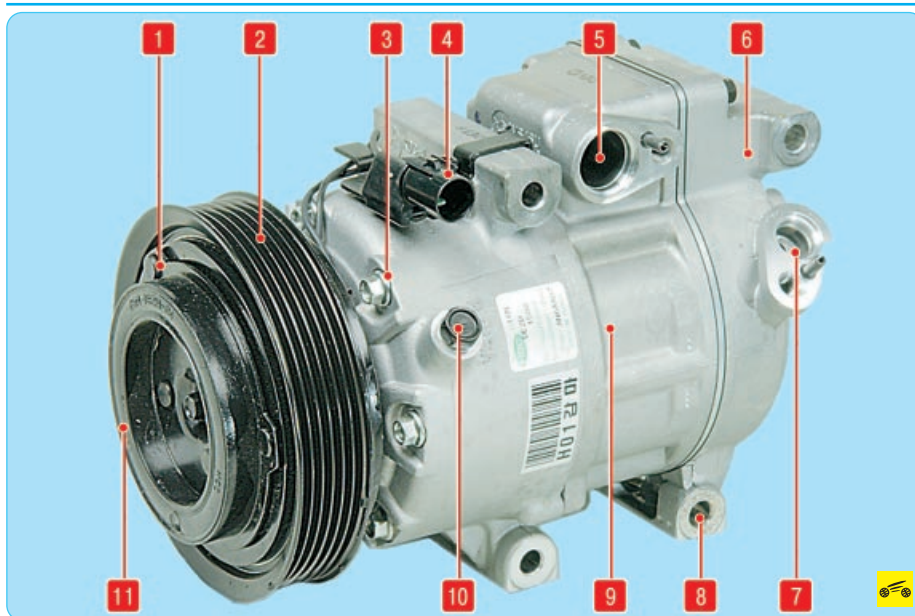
Компрессор кондиционера: 1 – прижимной диск; 2 – шкив привода; 3 – передняя крышка корпуса; 4 – колодка электрического разъема катушки электромагнита; 5 – фланец крепления трубопровода низкого давления; 6 – крышка блока клапанов; 7 – фланец крепления трубопровода высокого давления; 8 – проушина крепления; 9 – корпус насосной части; 10 – заглушка наливного отверстия; 11 – демпфер прижимного диска
